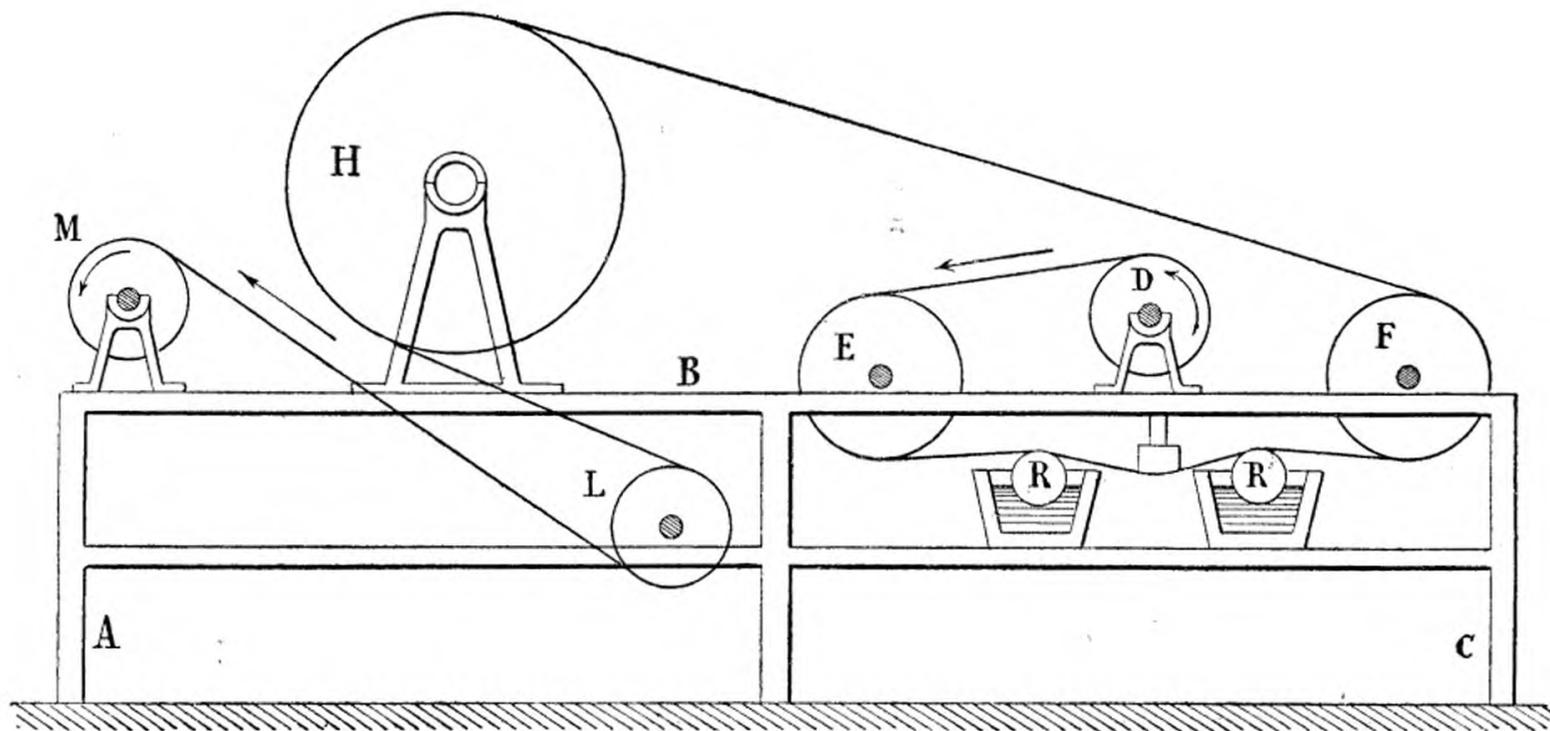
MACHINE A VULCANISER LES TISSUS
